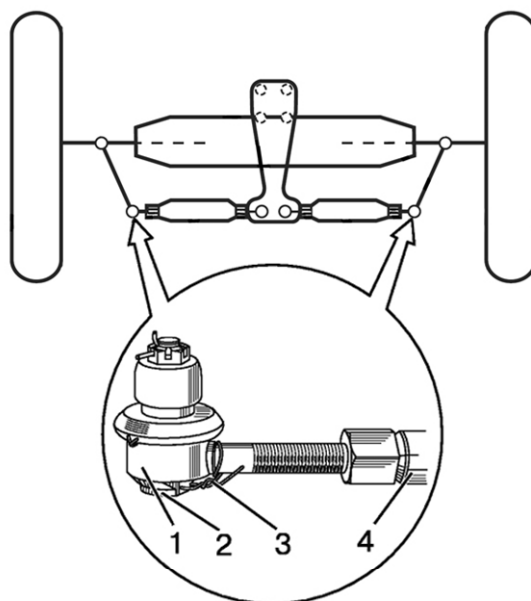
Проверка свободного хода рулевого колеса
